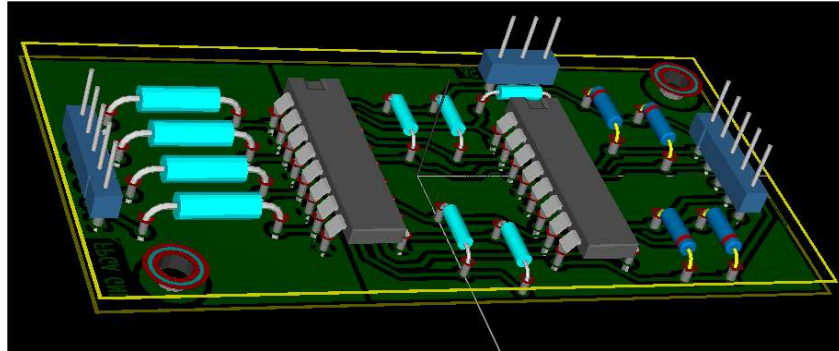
Imagen 3D del diseño de la PCB de control de los motores
